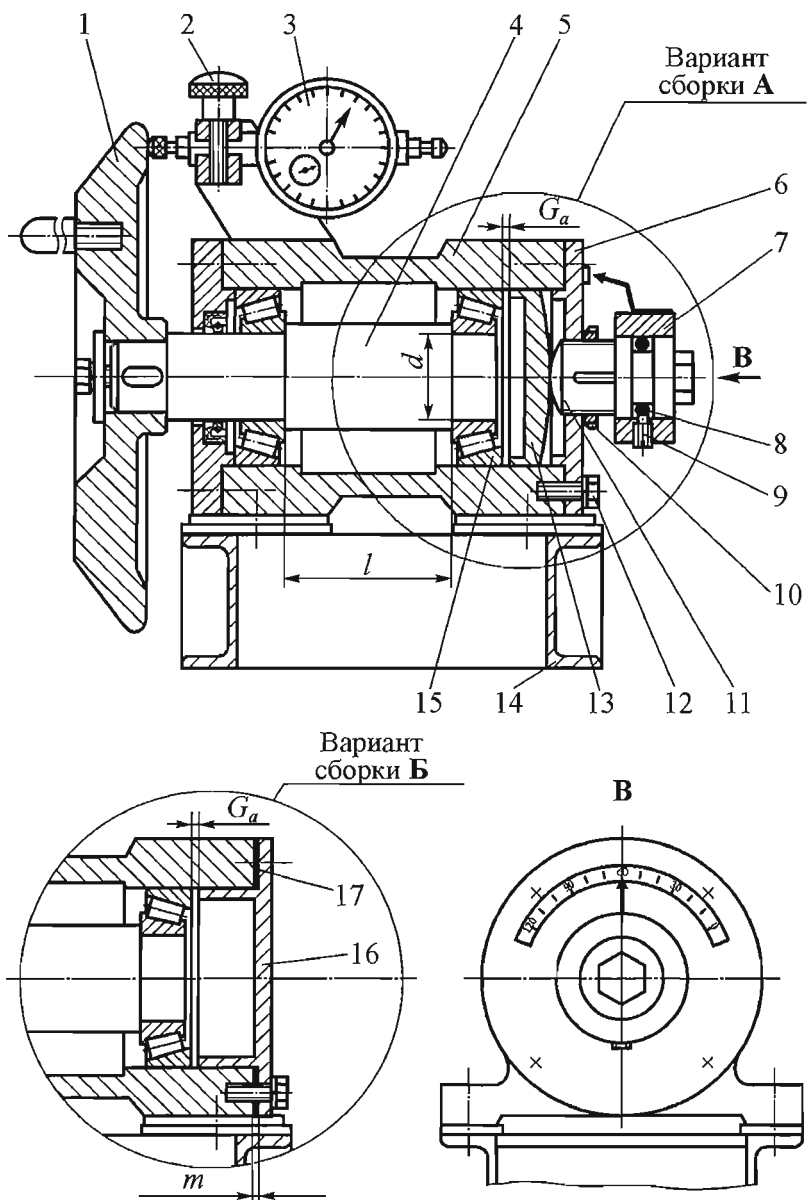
Конструкция лабораторной установки при установке подшипников по схеме II
